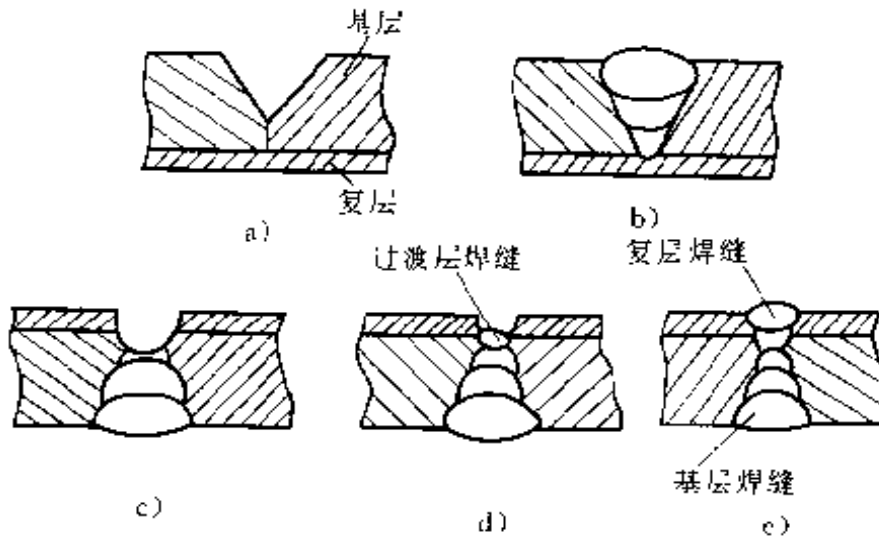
不锈钢复合钢板的焊接顺序
